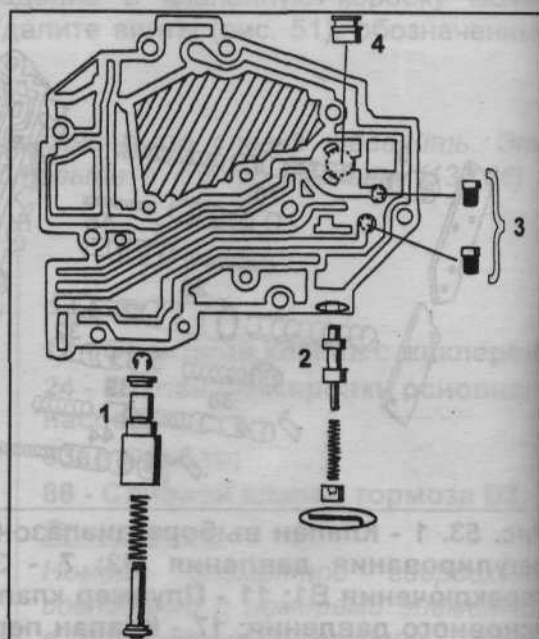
Нижняя часть клапанной коробки. 1 - Клапан блокировки рычага выбора диапазона; 2 - Клапан включения вспомогательного насоса; 3 - Фильтры; 4 - Клапан.
